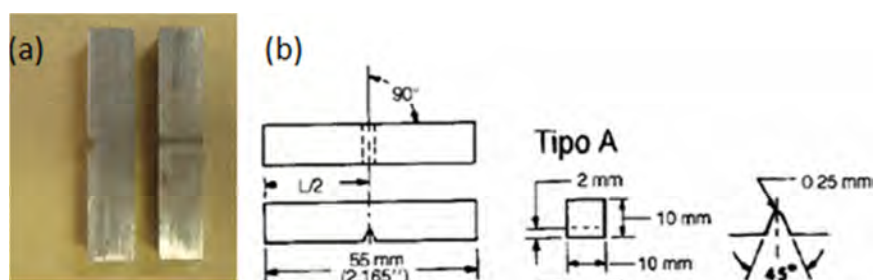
CPs usinados para ensaio de impacto (a) e desenho técnico (b).
